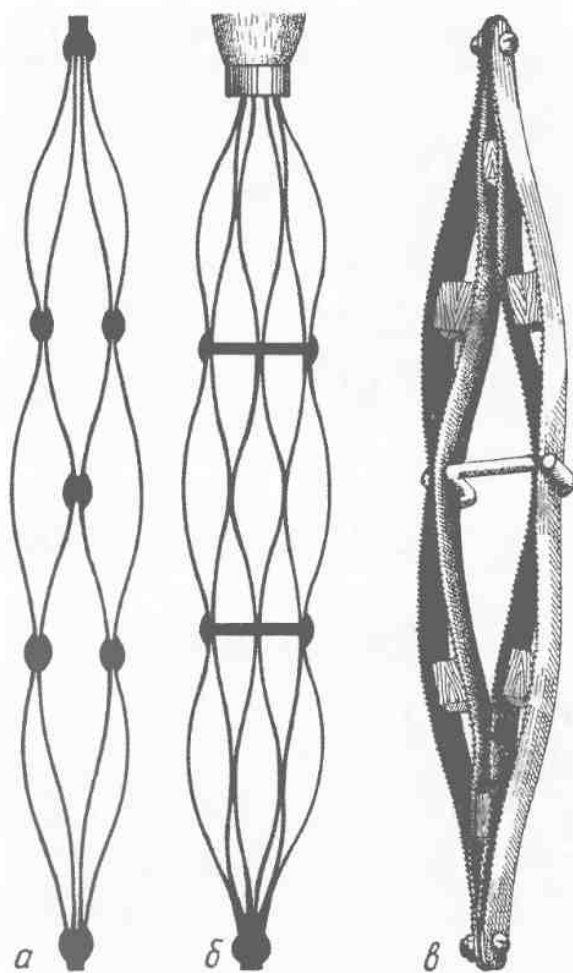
Рашпили для обработки древесины, смонтированные из ножовочных полотен для металла: а — из четырех полотен, соединенных попарно заклепками или болтиками; б — из шести полотен, соединенных заклепками или болтиками; в — из четырех полотен, соединенных с помощью металлической и деревянных распорок без сверления отверстий
